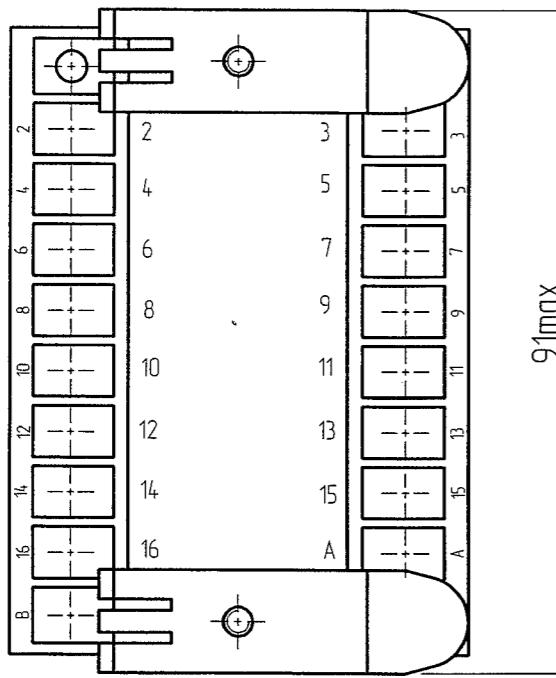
Реле типов PCB18-11-XXXX3; PCB18-12-XXXX3
